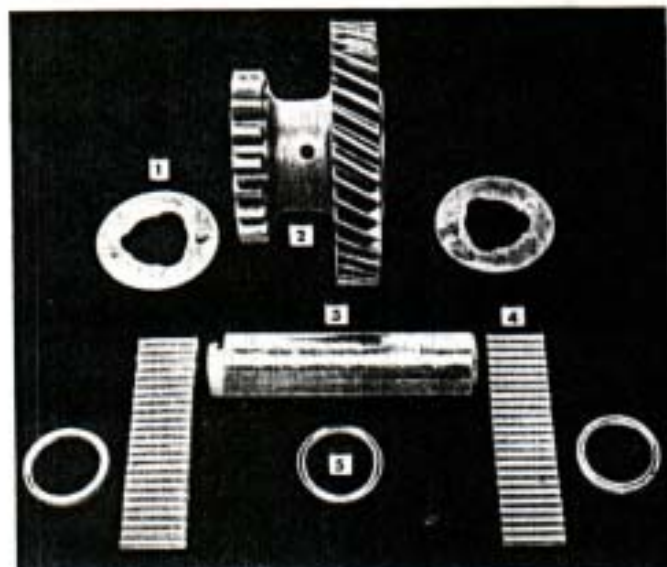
Conjunto del engranaje intermedio de la Caja de Transferencia. 1) Arandela de empuje. 2) Engranaje intermedio. 3) Eje del engranaje intermedio. 4) Rodillos del cojinete del engranaje intermedio. 5) Arandelas espaciadoras del cojinete.
